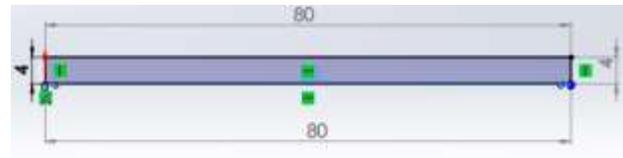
2Dimensi Hollow stainless steel 60 cm
